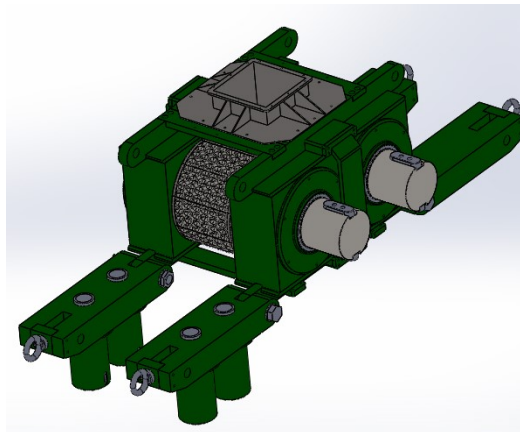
Desmontaje de los elementos de protección. (Fuente: propia)
